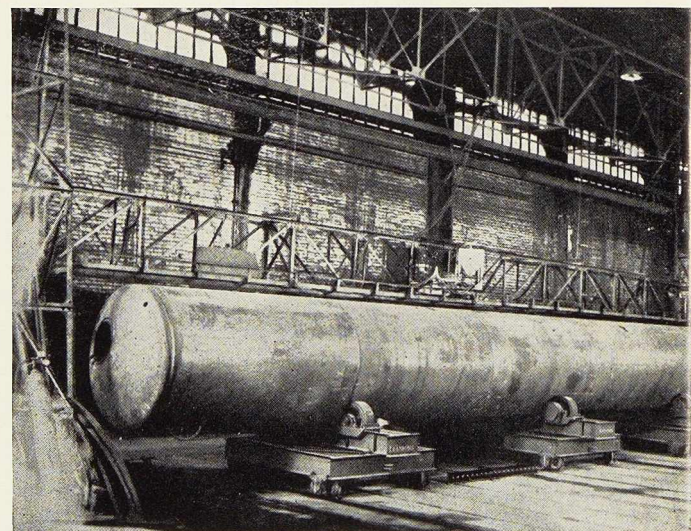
Soudage de réservoirs, en tôle de 7 mm d'épaisseur. La tête de soudage est placée sur une charpente, le réservoir est posé sur un montage pour l'exécution des soudures circulaires. (Constructeur : John Cockerill à Seraing.)
